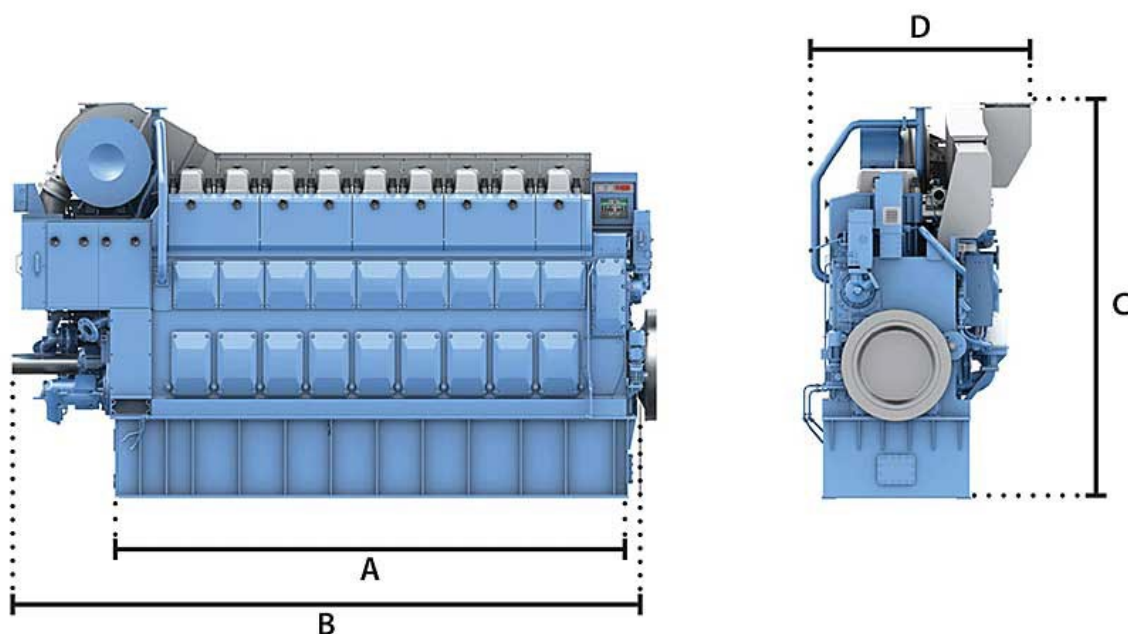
Габаритні розміри двигуна Rolls-Royce C26:33L6
